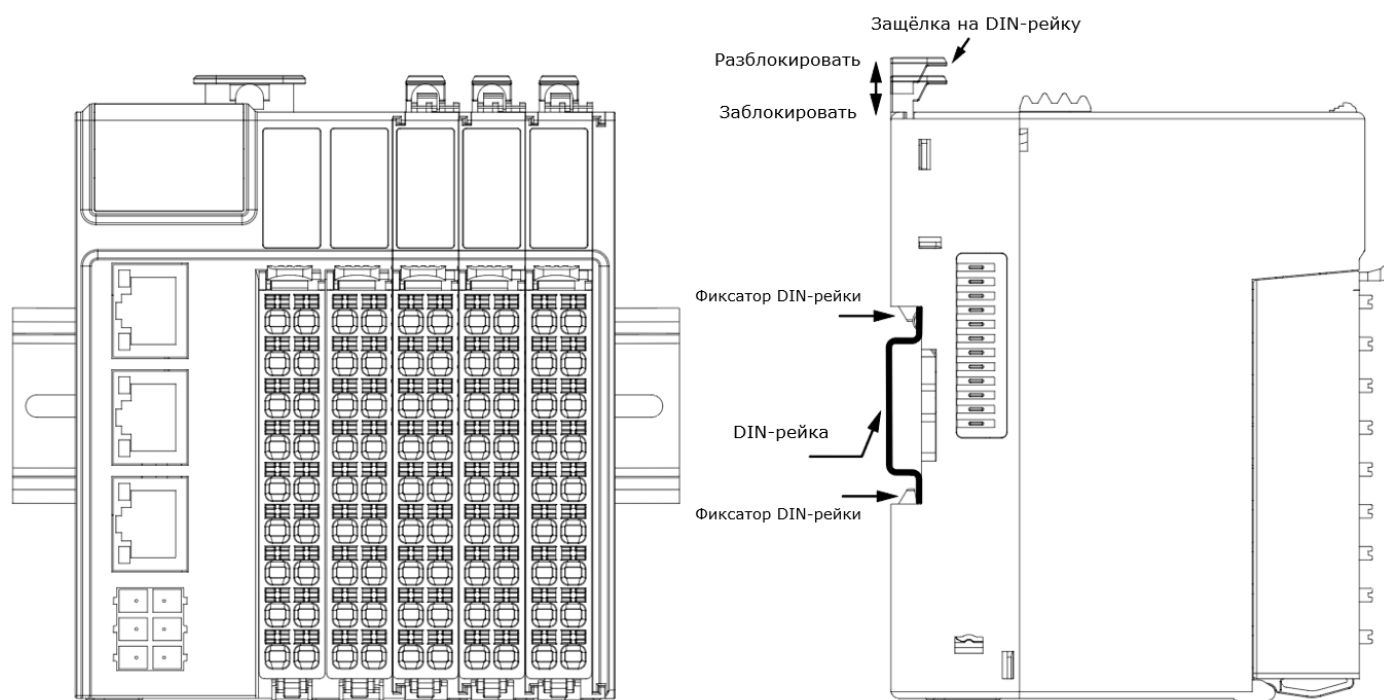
Первый шаг установки сборки устройств на DIN-рейку
